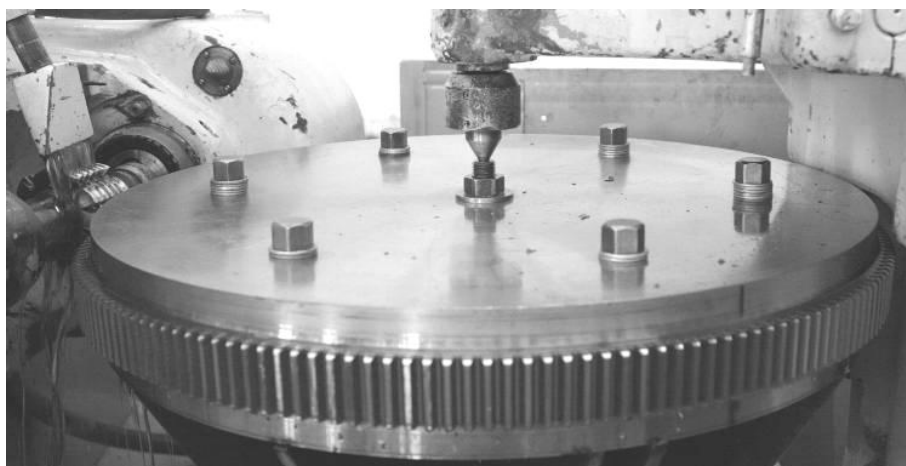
Нарезание зубчатого колеса червячной фрезой
